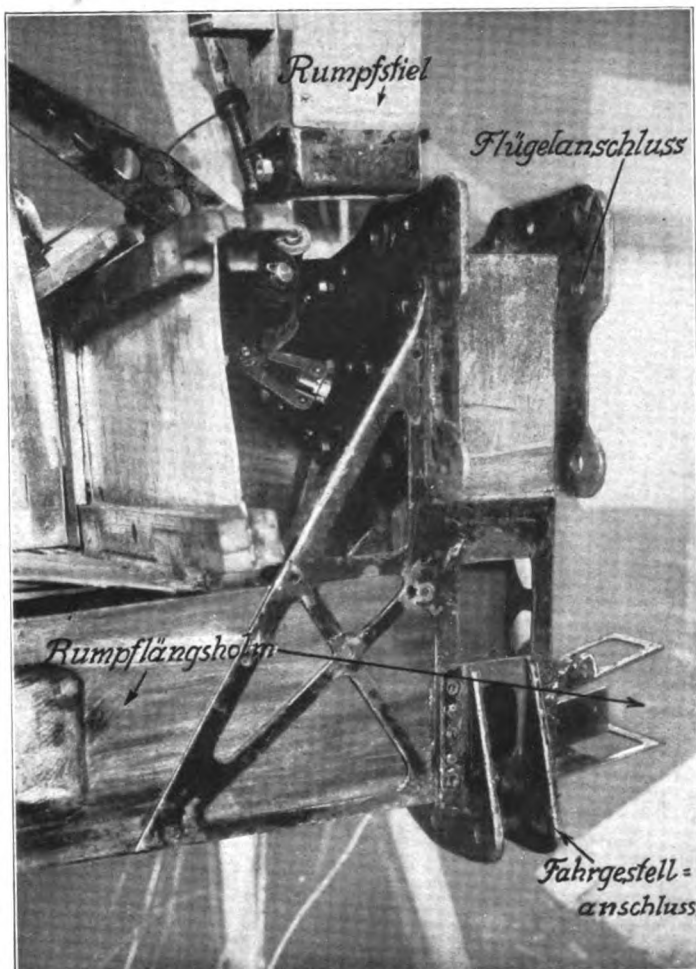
Handley-Page-G-Flugzeug. Holmbeschläge.
